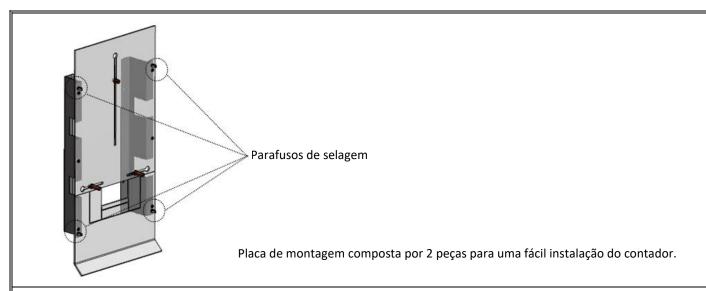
Pormenor da placa de montagem do contador - ECCE
